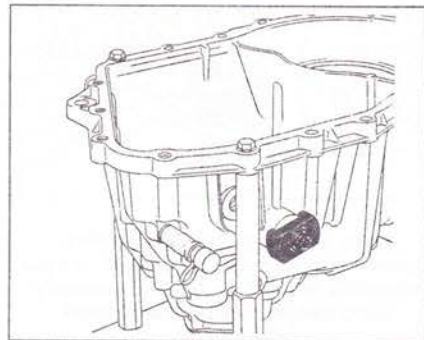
Установите подшипники при помощи приспособления В. Vi. 1510-01, индекс R.
